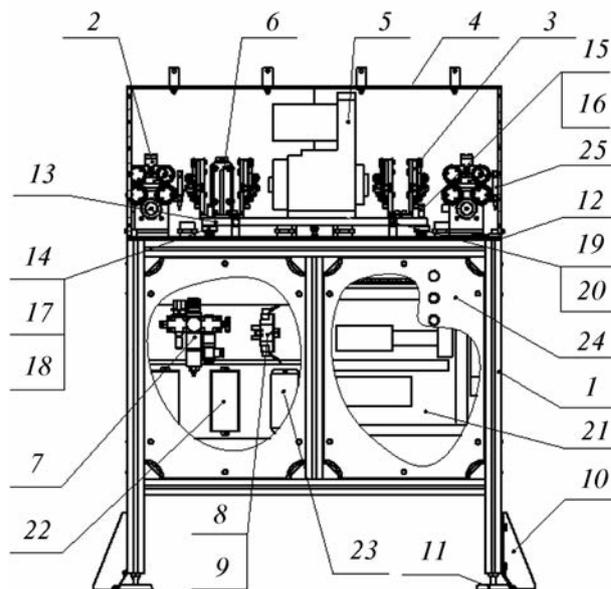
Механическая часть вихретоковой системы ELO 3T: 1 — стол; 2 — протяжка; 3 — центратор; 4 — укрытие; 5 — датчик ЕС; 6 — блок ВТП; 7 — блок подготовки воздуха; 8 — пневмораспределитель; 9 — глушитель; 10 — фундаментный угловой соединитель; 11 — регулируемая опора; 12 — плита; 13 — плита (регулируемая); 14 — шпилька; 15 — гайка (фиксирующая); 16 — шайба; 17 — гайка (регулирующая); 18 — шайба; 19 — винт (регулирующий); 20 — гайка (контргайка); 21 — монтажная панель; 22 — частотный преобразователь двигателя протяжки; 23 — частотный преобразователь двигателя датчика ЕС; 24 — панель стола; 25 — датчик наличия изделия
